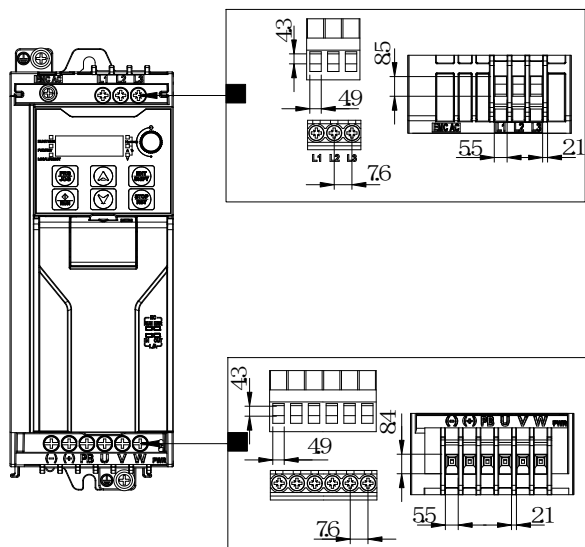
Клеммы главной цепи (Типоразмер типа С)
